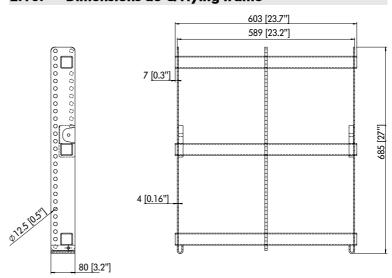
Dimensions en mm du Z5159 Q Flying frame
